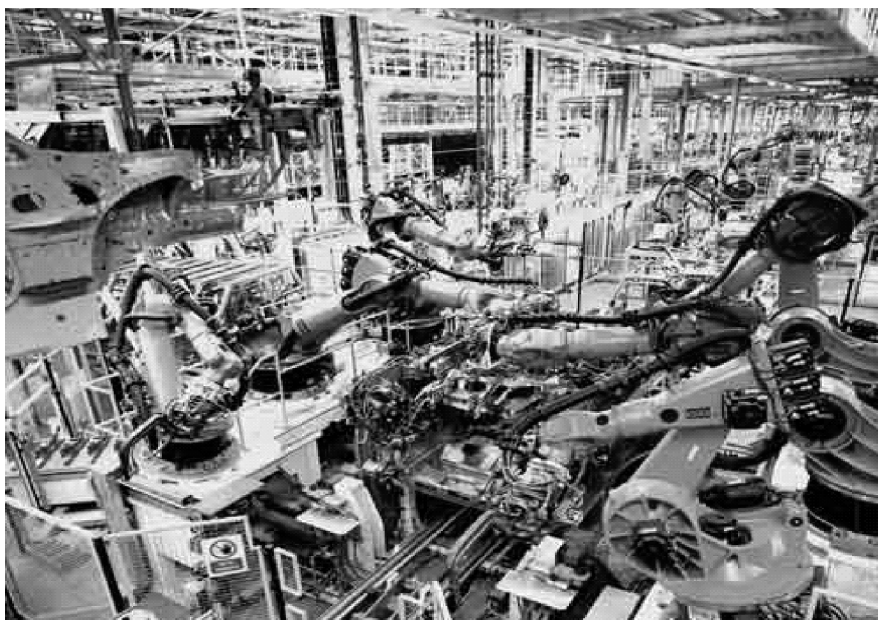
白车身总成合拼装的点（定）焊工位
